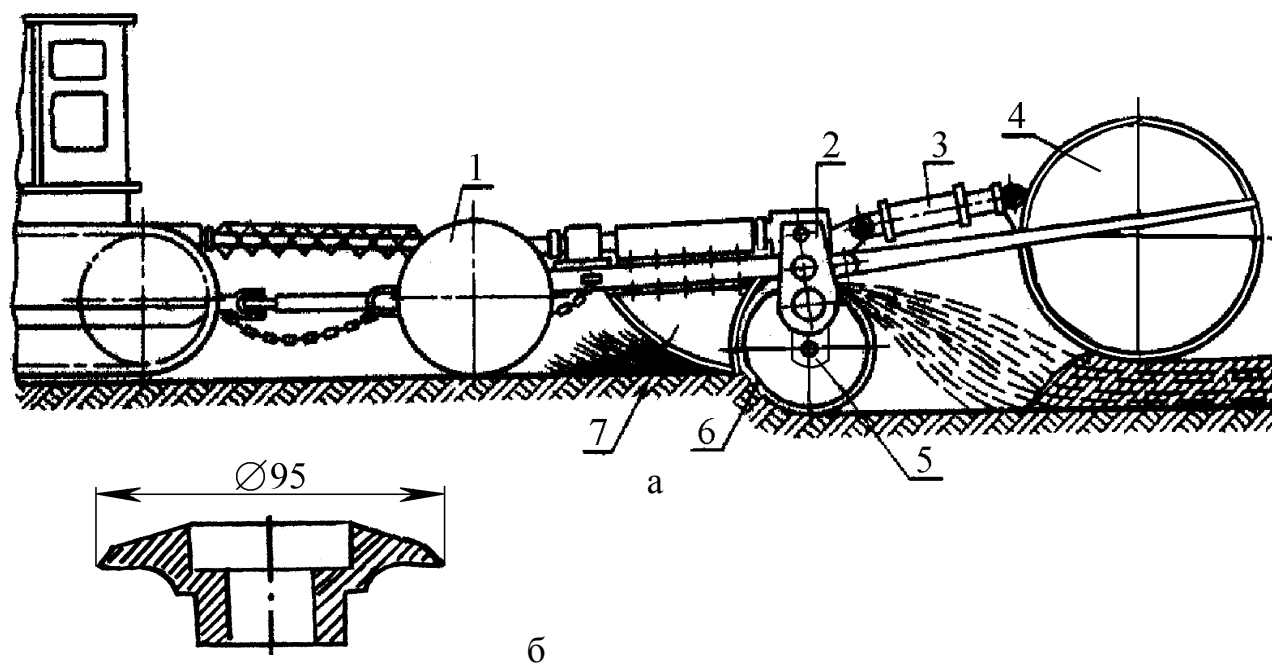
Машина для глибокого фрезерування МТП–42
